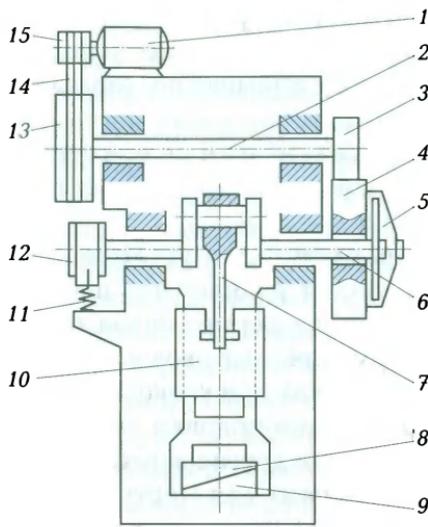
Кинематическая схема горячештамповочного кривошипного прессы:
